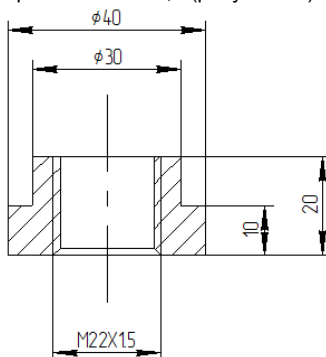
Габаритные и присоединительные размеры патрубка дренажа
